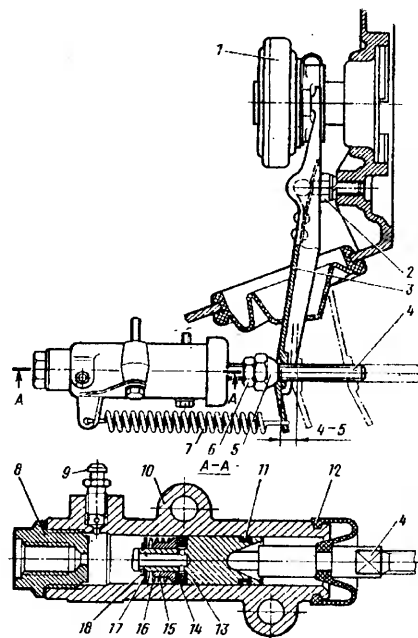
Рабочий цилиндр и вилка выключения сцепления:
